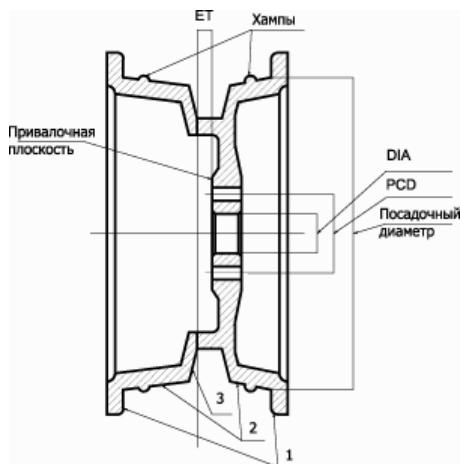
Неразборный диск: 1 – закраины; 2 – полки; 3 – ручей
